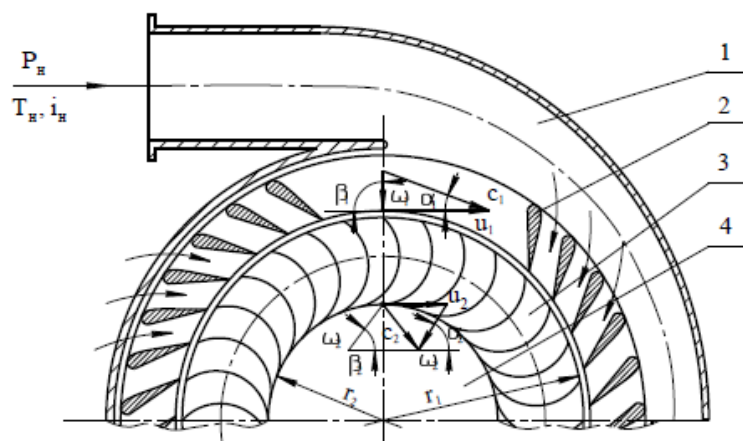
Движение потока в рабочем колесе турбодетандера
